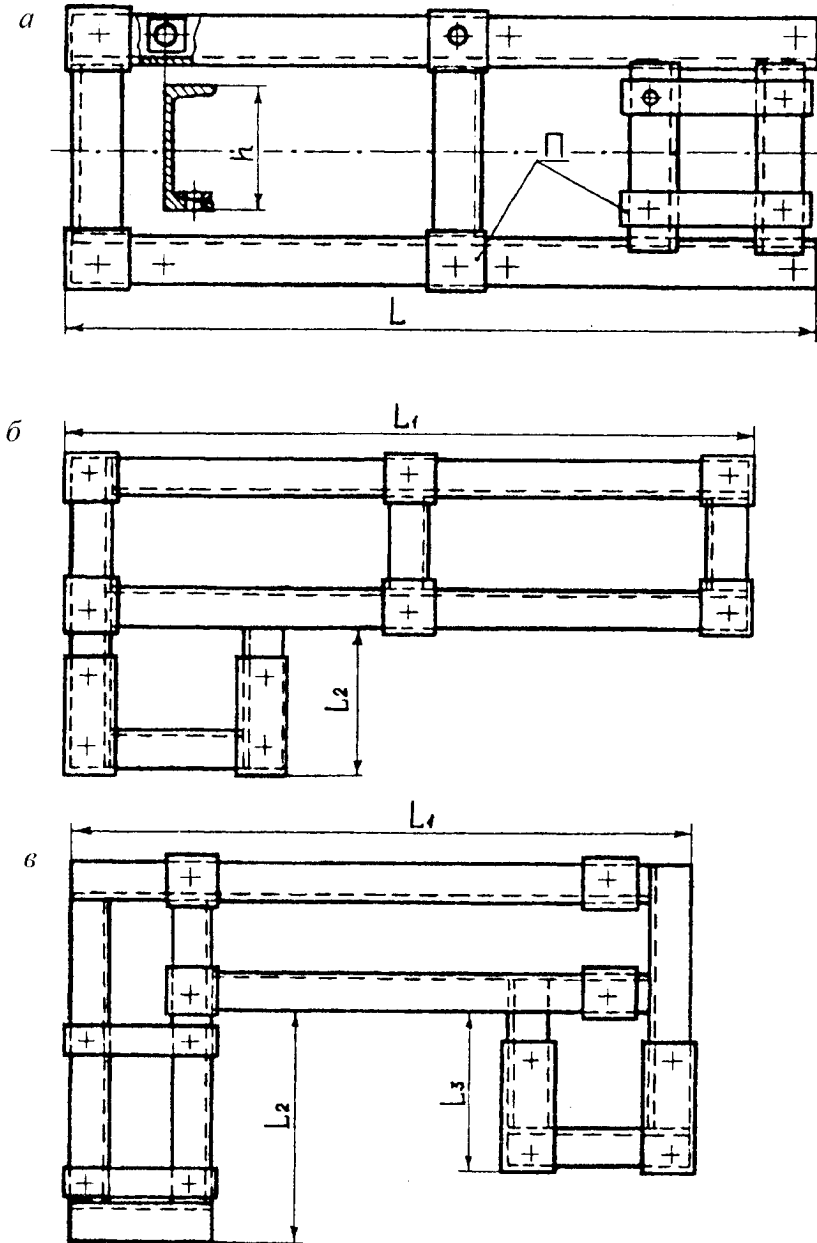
Взірці зварних рам для розміщення редуктора і двигуна:
